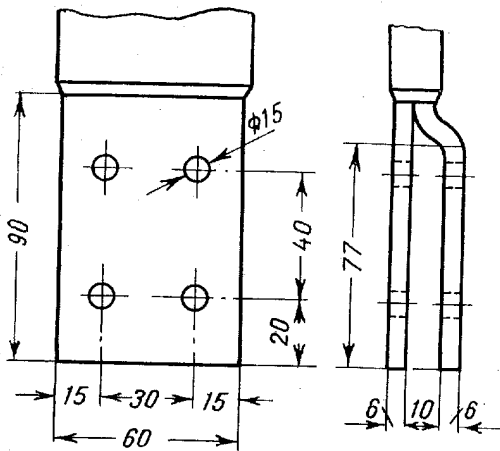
Размеры выводных пластин обмотки статора электродвигателя типа SM-6000-2
